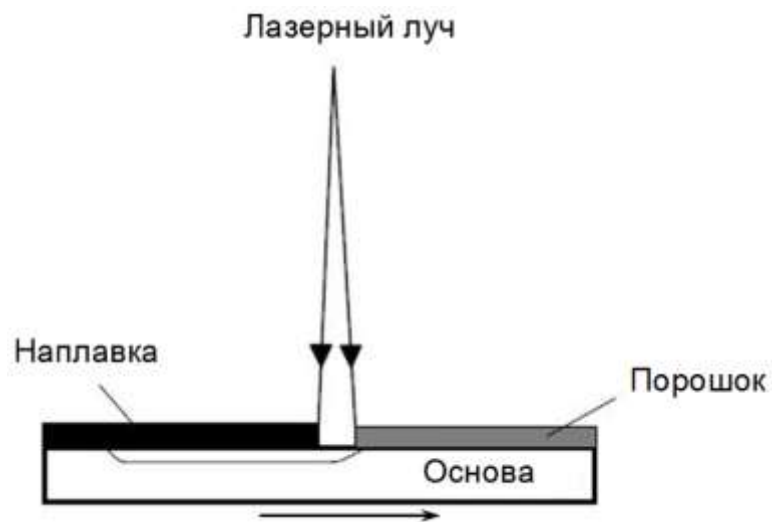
Схема двухступенчатой лазерной наплавки
